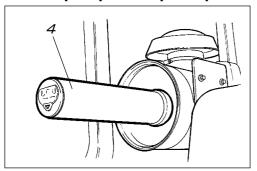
Воздушный фильтр 4. Резервный фильтр
